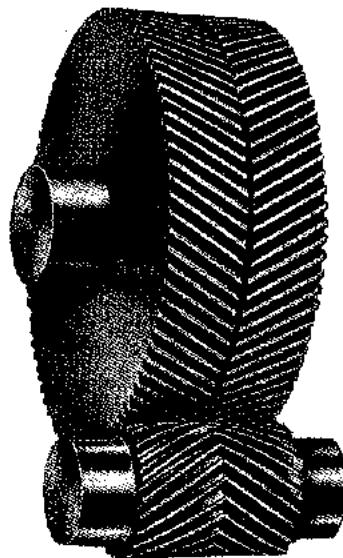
Engranaje doble helicoidal. (Philadelphia Gear Works)
